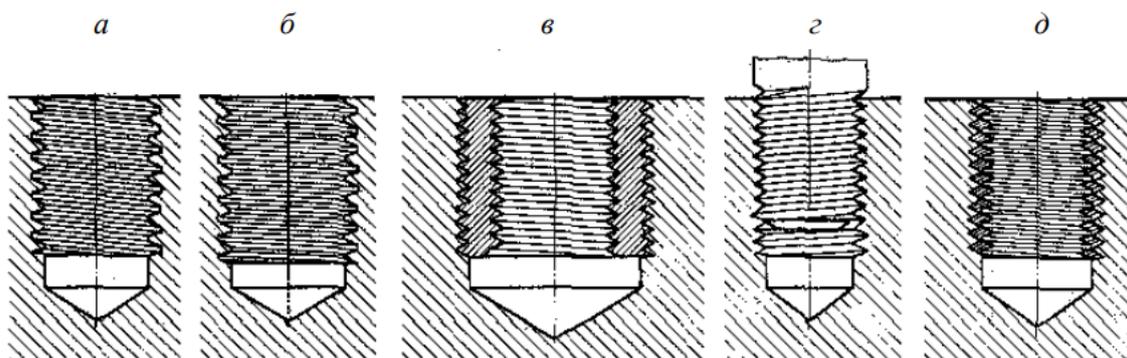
Способы ремонта резьбовых соединений:
